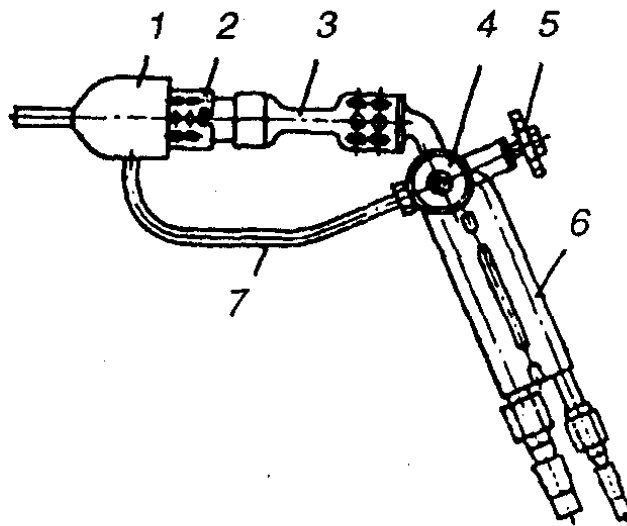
Пропано-воздушная горелка для сварки пластмассовых оболочек:
